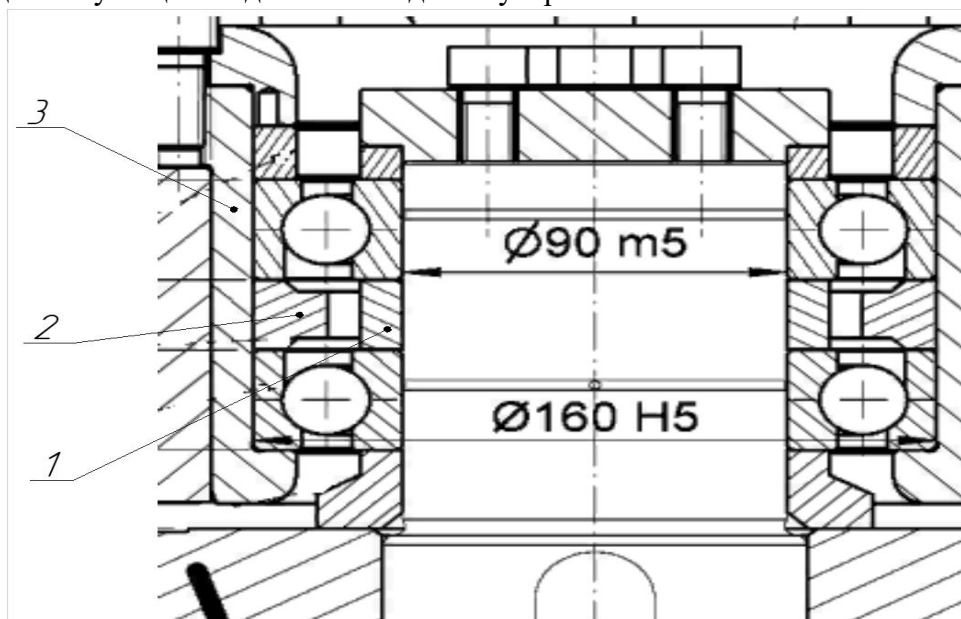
фрагмент чертежа редукторной части клетки после реконструкции
